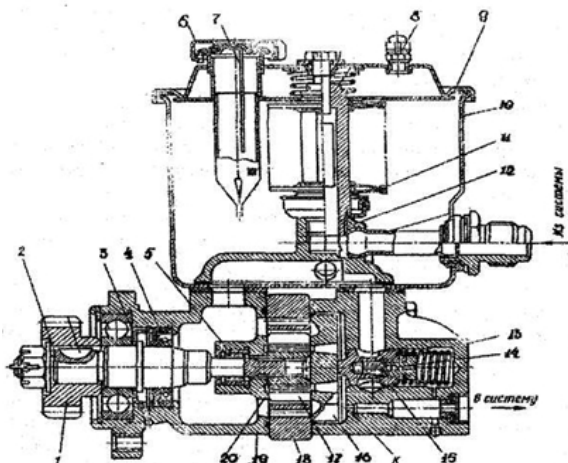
Насос гидроусилителя: 1 - шестерня; 2 - вал; 3 - кольцо; 4 - сальник; 5 - игольчатый подшипник 6 - крышка; 7 - указатель уровня масла; 8 - предохранительный клапан; 9 - прокладка; 10 - бачок ;11 - сетчатый фильтр; 12 - коллектор ; 13 - крышка; 14 - предохранительный клапан; 15 - перепускной клапан; 16 - распределительный диск; 17 - лопасть ; 18 - статор; 19 - корпус; 20 ротор; К - Калиброванное отверстие.
